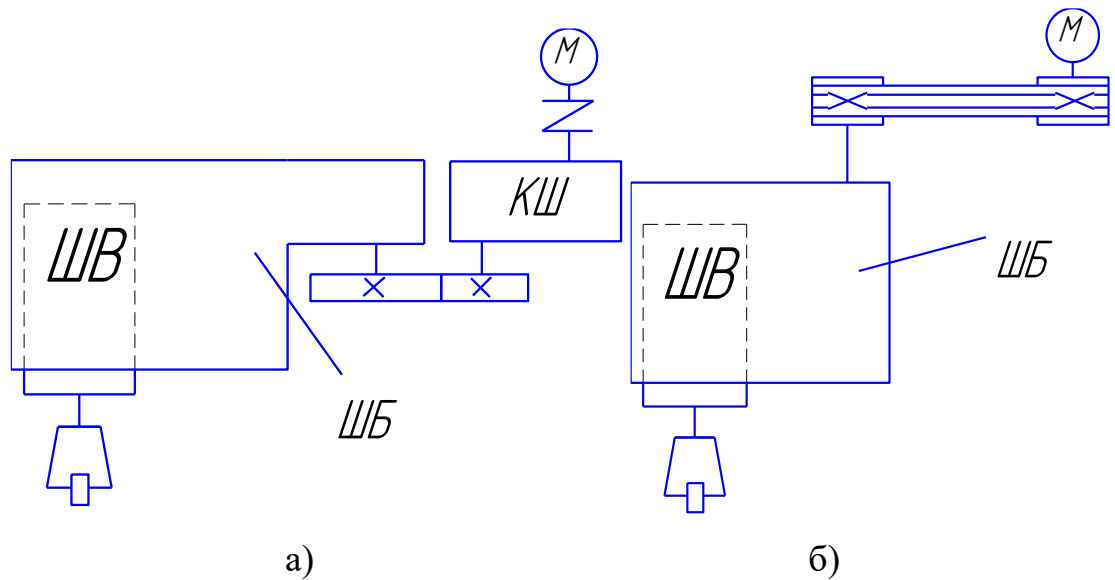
Структури приводів фрезерних верстаті з коробками швидкостей
